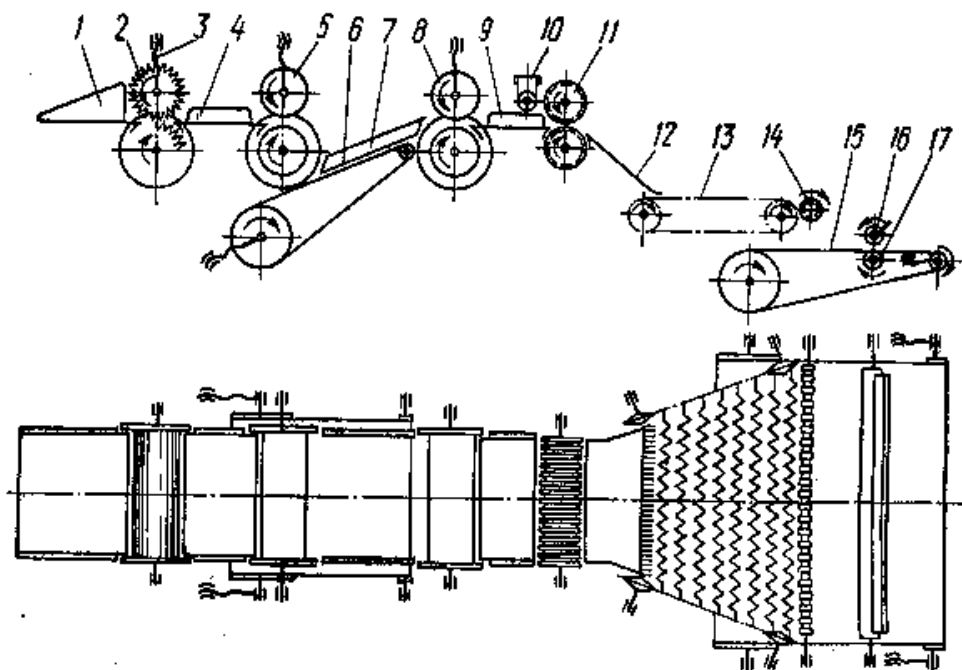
Схема формувальної машини ХФБ для виробництва хлібних паличок: 1 – приймальний лоток з боковими обмежувачами; 2 – приймальні рифлені валки з ребордами для натирання тіста; 3- механізм регулювання зазору між валками; 4,9 – напрямний лоток з боковими обмежувачами; 5 – перша пара розкочувальних валків з ребордами; 6 – проміжний транспортер; 7 – бокові обмежувачі; 8 – друга пара розкочувальних валків; 10 – механізм посипання; 11 – різальні валки з профільними канавками; 12 – гребінка; 13 – ланцюговий опахалоподібний розвідний конвеєр; 14 – калібрувальний валок вирівнювач кроку; 15 – стрічковий передавальний конвеєр; 16 – ніж для відрізання; 17 – підпірний валок.
